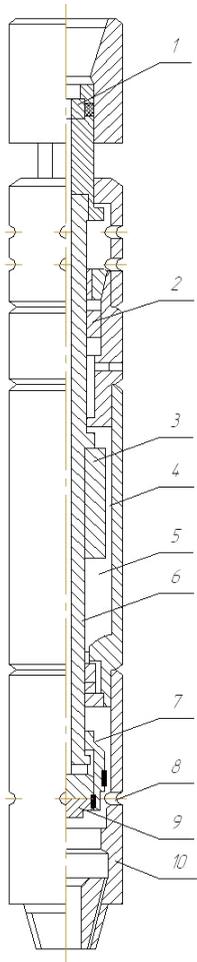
Схема многоциклового испытателя пластов ИПМ-2: 1 – сменный штуцер; 2 – подвижное уплотнение; 3 – тормозной поршень; 4 – калибровочные каналы; 5 – тормозная камера; 6 – подвижный шток; 7 – запорная гильза; 8 – отверстия уравнильного клапана; 9 – впускной клапан; 10 – нижний переводник
